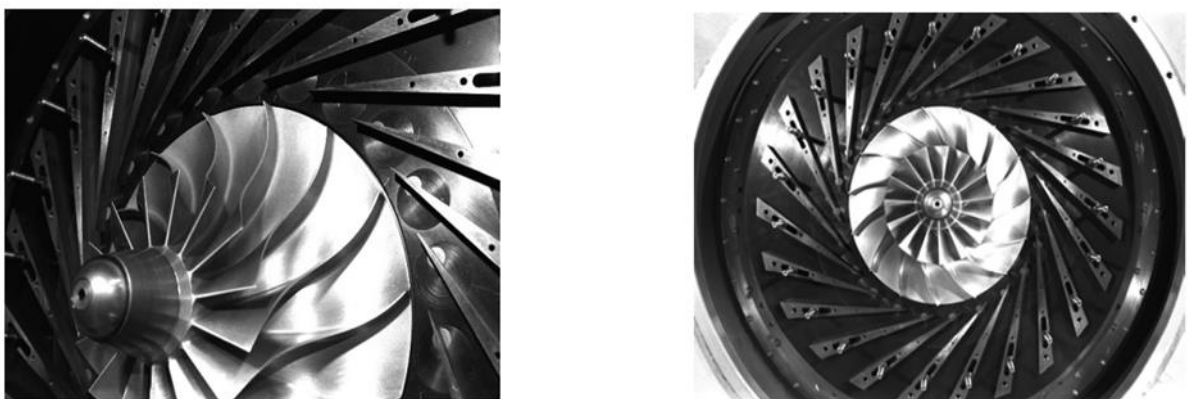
Stadio del compressore con parete frontale rimossa
